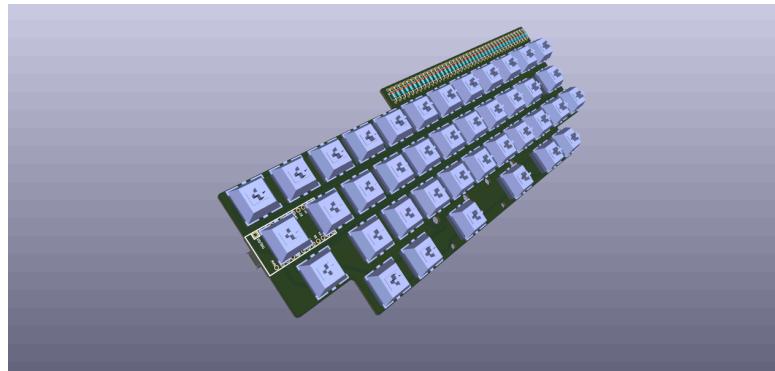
PCB TCBK40 no visualizador 3D, Kicad
